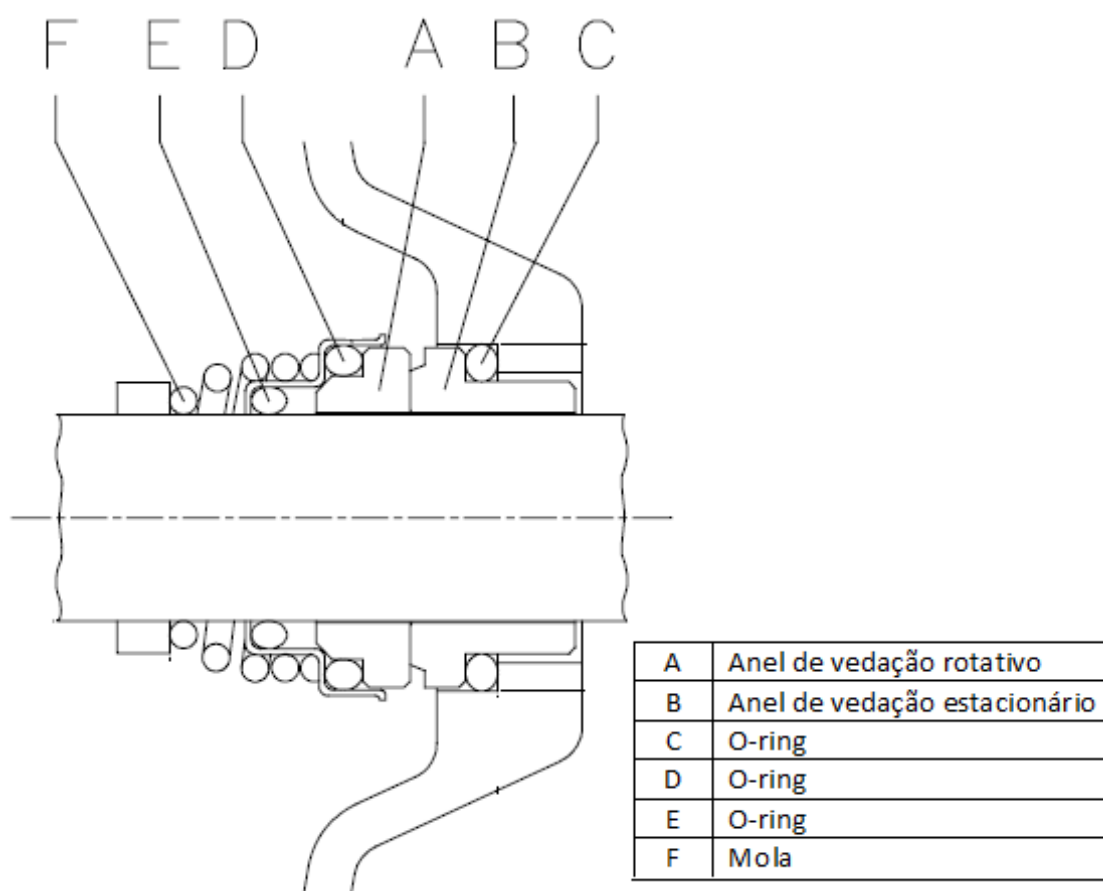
Desenho técnico da vedação mecânica ^[104]
